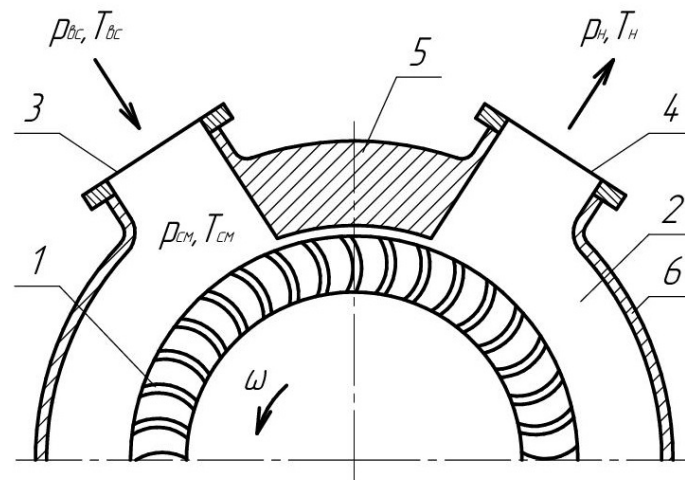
Схема вихревой ступени с двусторонним периферийно-боковым каналом, боковыми серповидными лопатками с покрывным диском:
